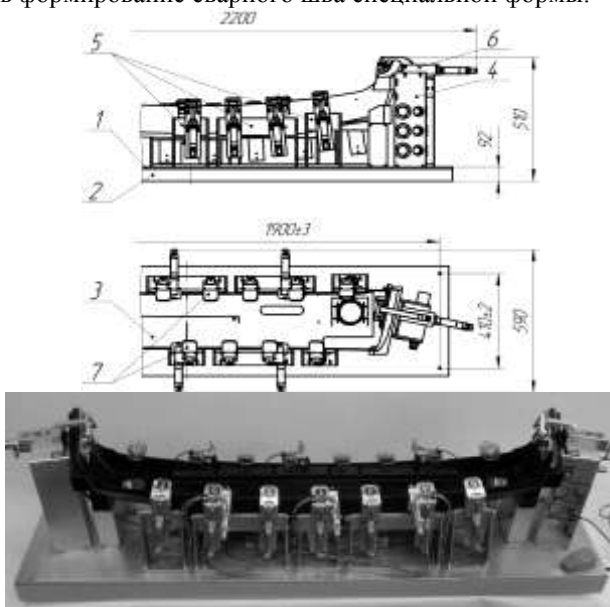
Система позиционирования сварочного инструмента:
